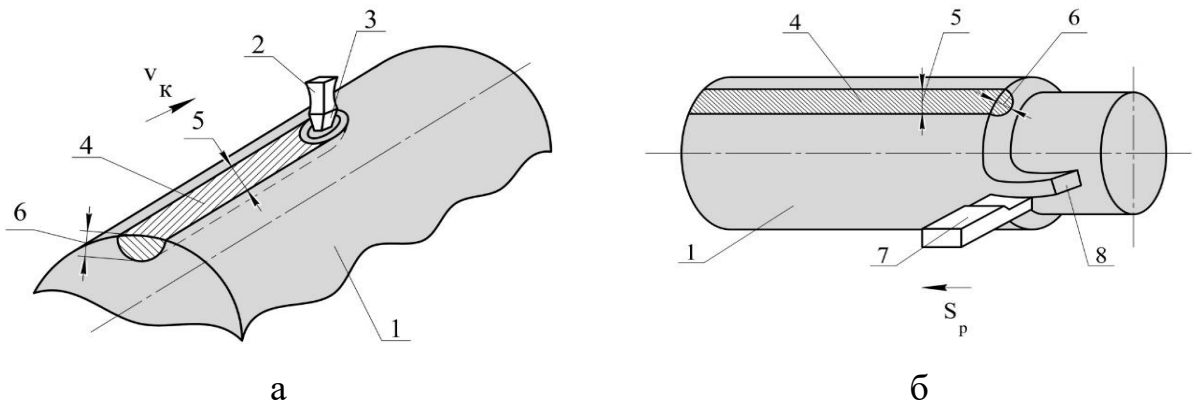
Способ механической обработки деталей типа «тел вращения» из сталей аустенитного класса (составлено автором): а – схема нанесения предварительного ЛКВ; б – схема процесса механической обработки с ЛКВ, где 1 – заготовка; 2 – устройство подачи жидким азотом; 3 – сопло устройства подачи жидкого азота; 4 – метастабильная структура; 5 – ширина упрочненной зоны; 6 – глубина упрочненной зоны; 7 – режущий инструмент; 8 – стружка
